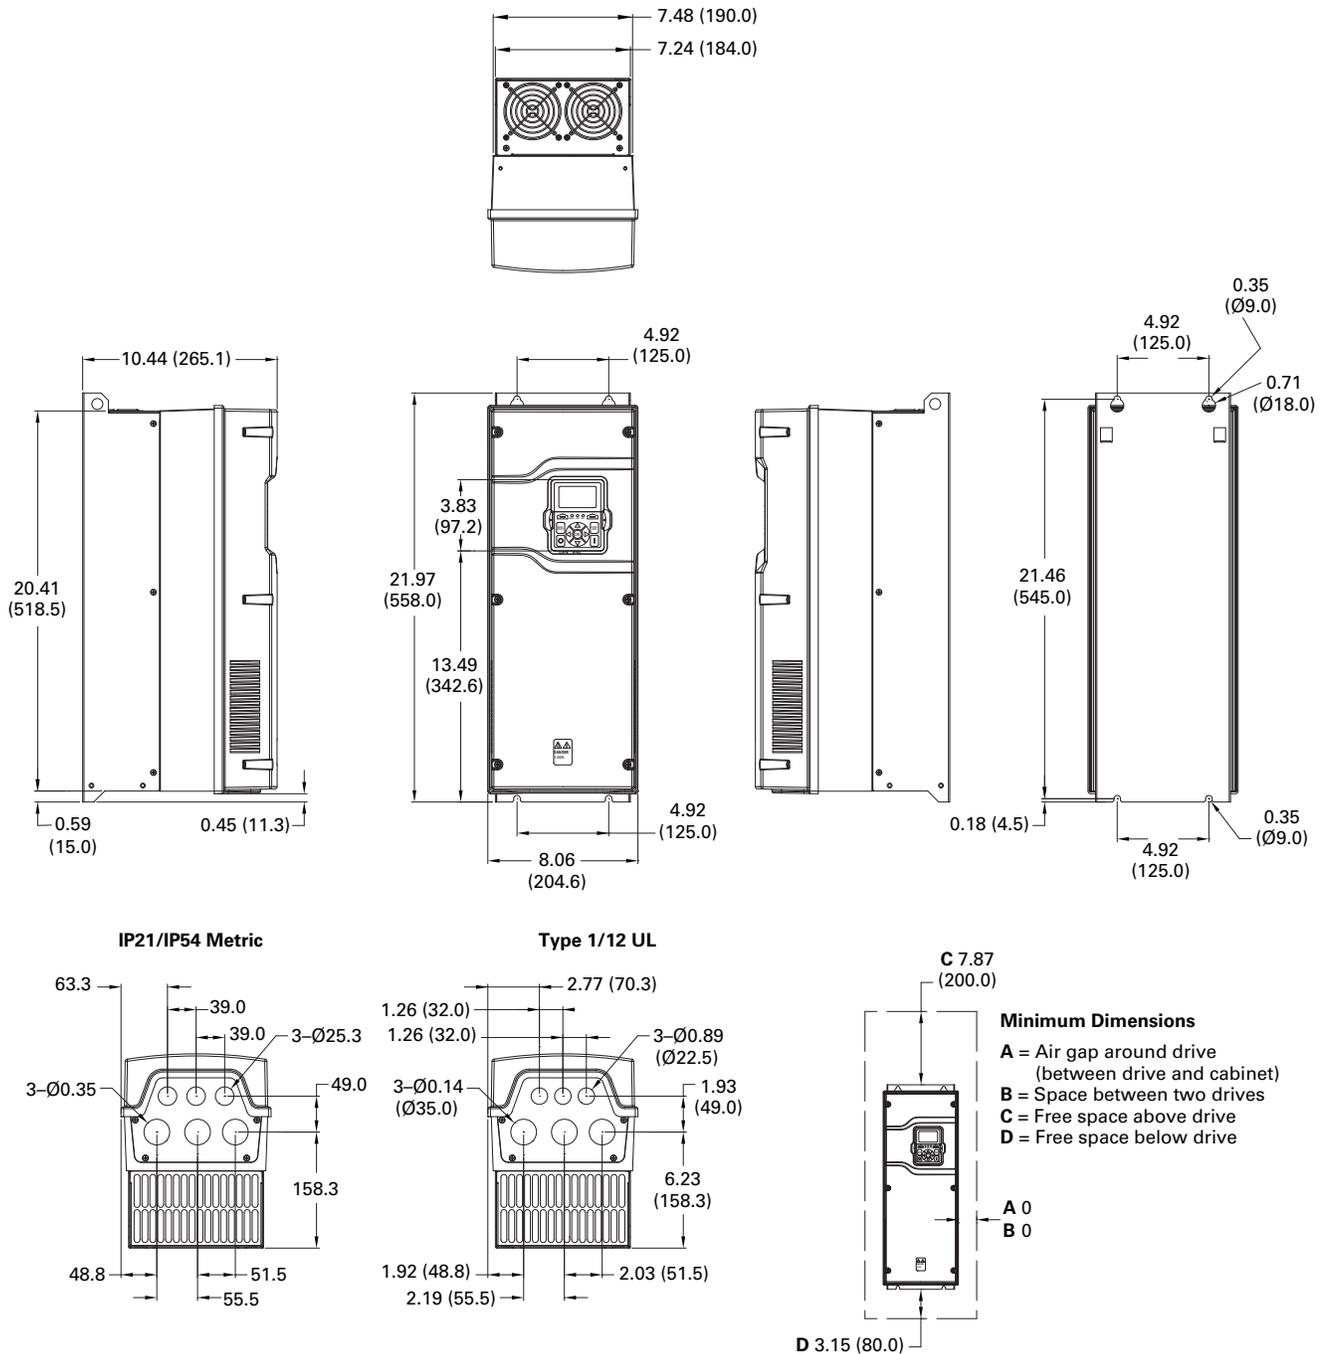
FR2 Abmessungsgrafik Flanschbefestigung
